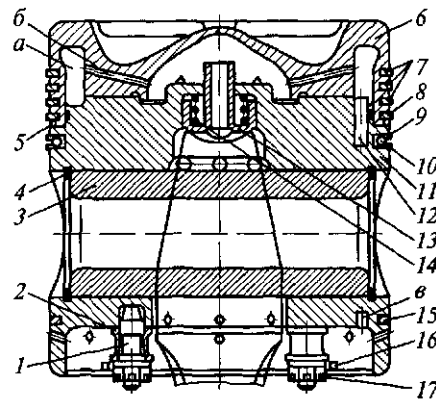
Поршень дизеля 1А-5Д49-2: 1 - шпилька; 2 - втулка; 3 - палец; 4 - стопорное кольцо; 5 - уплотнительное кольцо; 6 - головка поршня; 7 - компрессионные кольца с односторонней трапецией; 8 - компрессионное (минутное) кольцо; 9, 15 - маслосъемные кольца; 10 - экспандер; 11 - тронк; 12 - трубка; 13 - стакан; 14 - пружина; 16 - проволока; 17- гайка; а - полость охлаждения днища крышки; б - отверстие для перетока масла; в - канал для слива масла из полости охлаждения.
